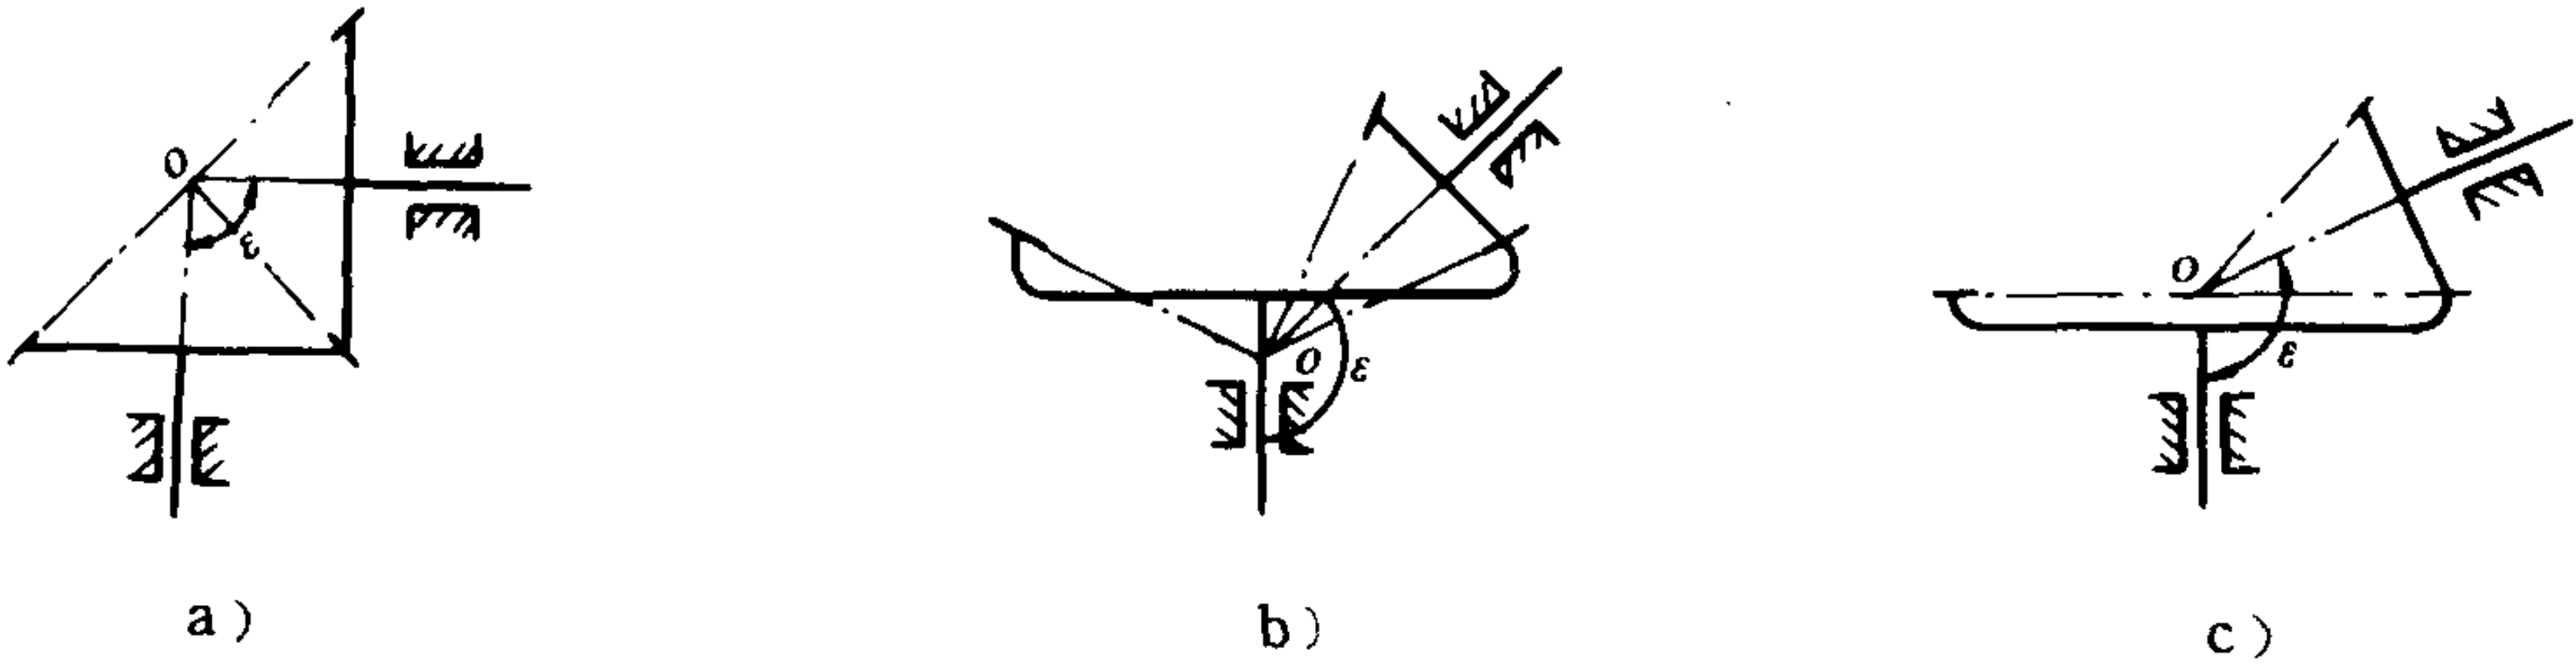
不同啮合形式的圆锥齿轮传动
